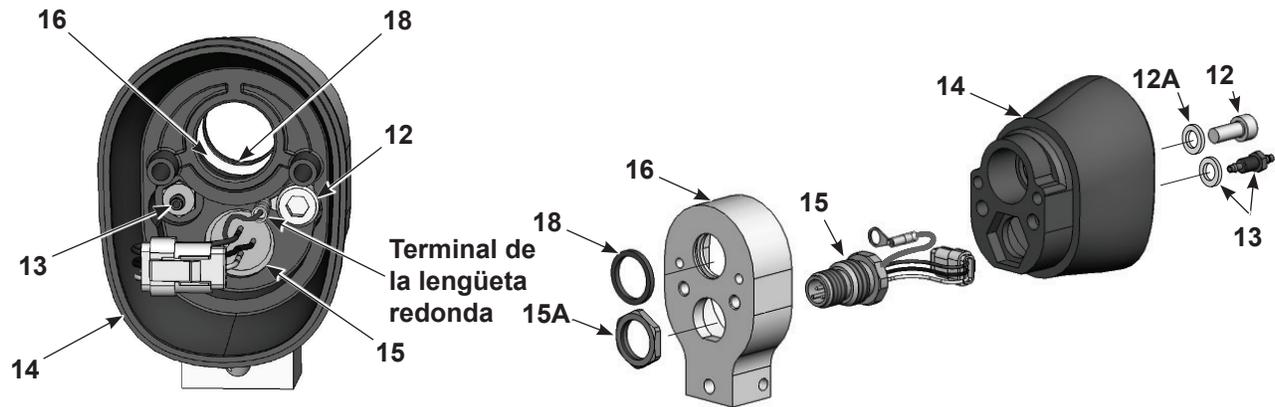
Desmontaje de una pistola de montaje en barra 3 de 3
